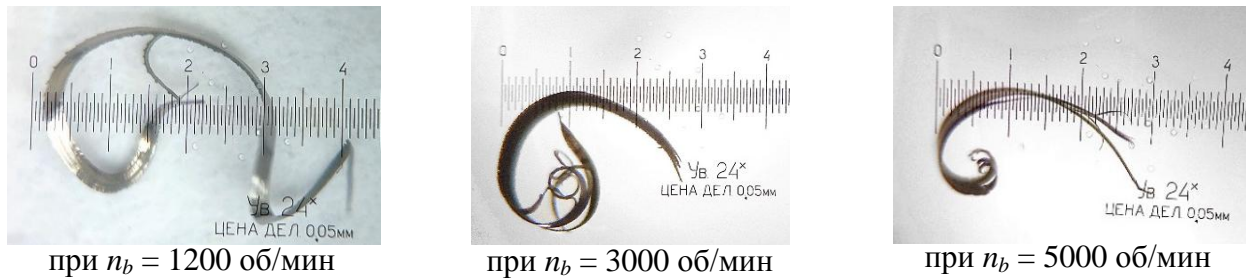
Образцы стружки при обработке заготовок из стали 20
